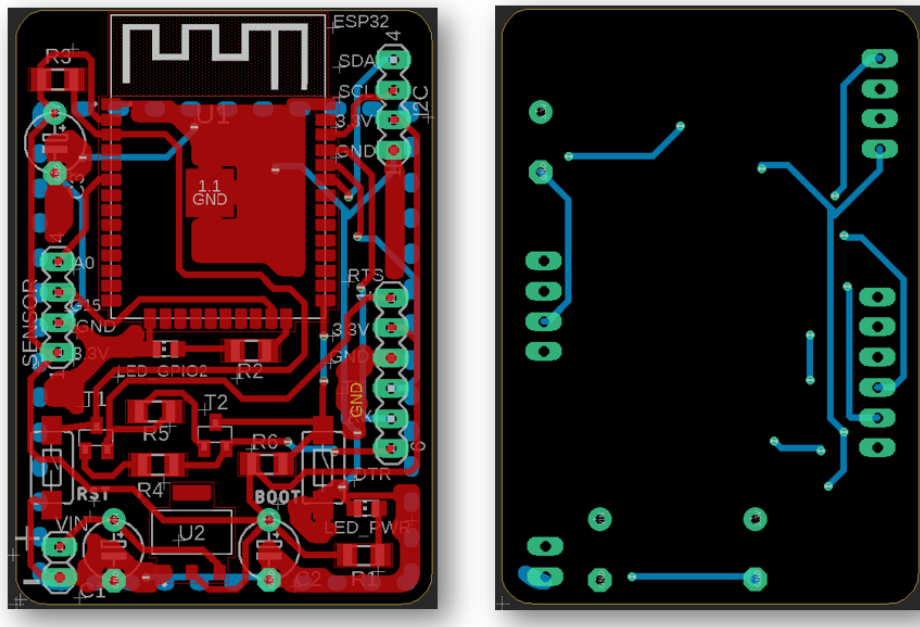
Diseño de la PCB ESP-32 en una placa base, izquierda: vista superior, derecha: vista inferior.
